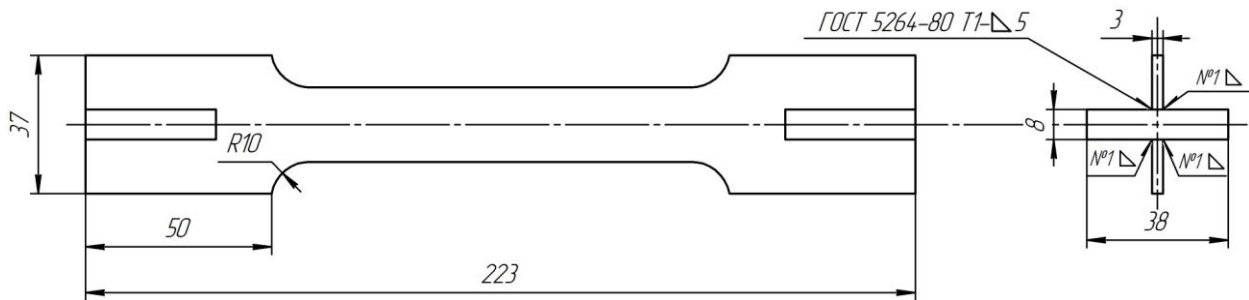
Чертеж образца из стали Ст3 для испытаний на одноосное растяжение.
